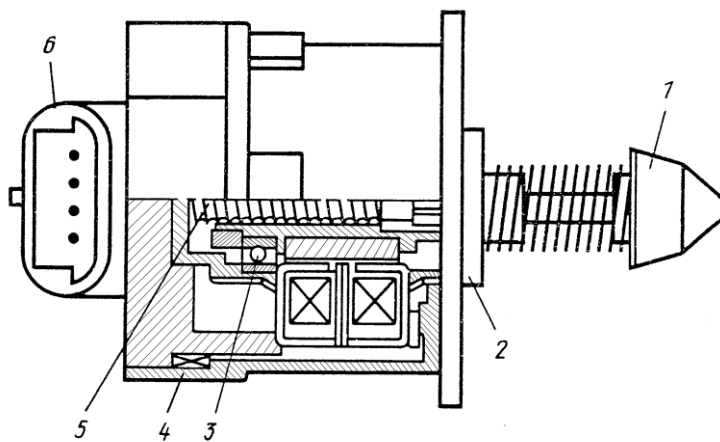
Конструкция регулятора холостого хода на базе шагового двигателя: 1 – конусный запирающий элемент; 2 – фланец крепления; 3 – подшипник; 4 – корпус регулятора; 5 – винтовая часть подвижного элемента; 6 – электрический разъем
